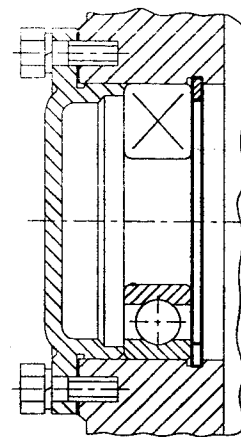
Закрепление наружного кольца подшипника качения в корпусе с использованием пружинного кольца
